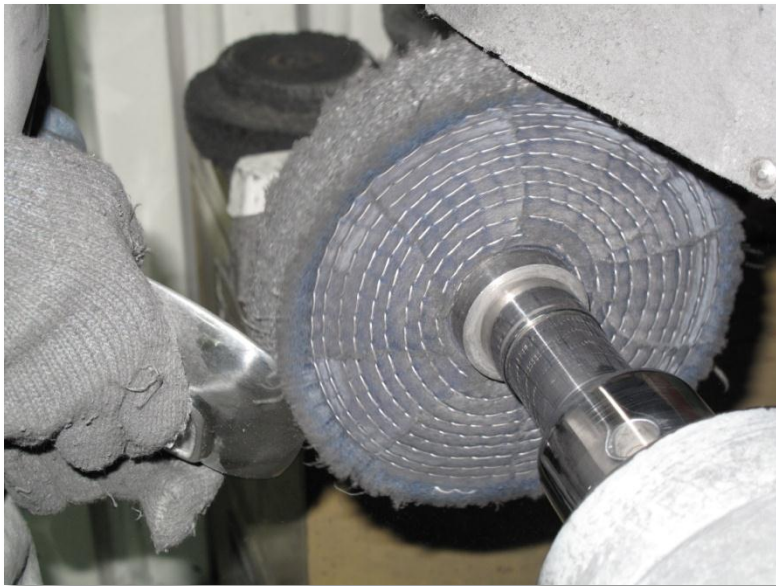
Pieza abrillantada, en la parte externa, con una manta de mayor tamaño.
